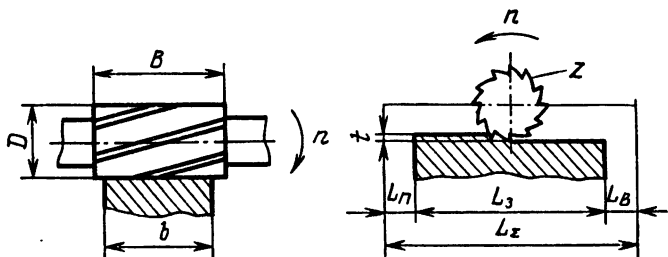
Схема фрезерования плоской поверхности цилиндрической фрезой
